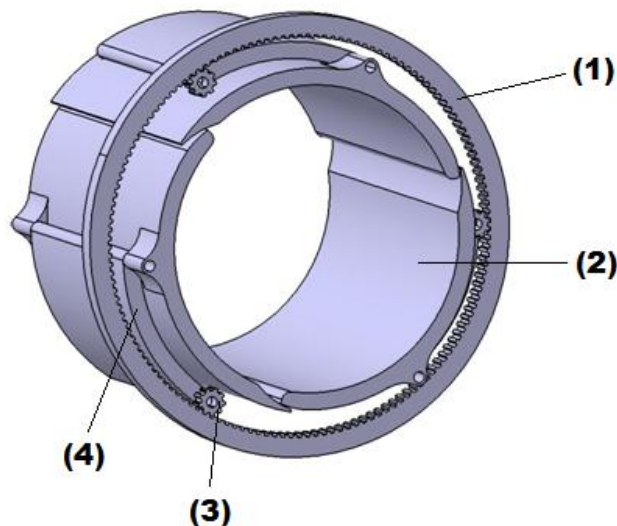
Principais componentes da solução de engrenagem: 1) Engrenagem de dentado recto de grande diâmetro, cremalheira; 2) Pás de compactação do lixo; 3) Engrenagens de diâmetro reduzido, pinhão; 4) Braços de transmissão de movimento.
